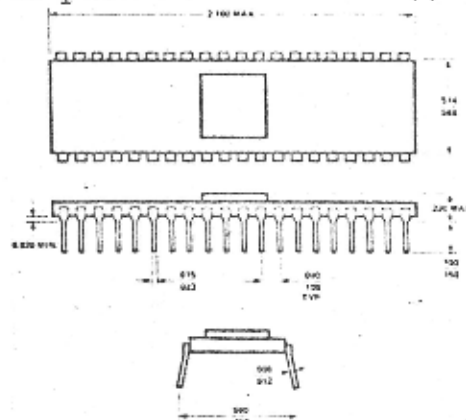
Схема 40-штырькового керамического корпуса с двух-
